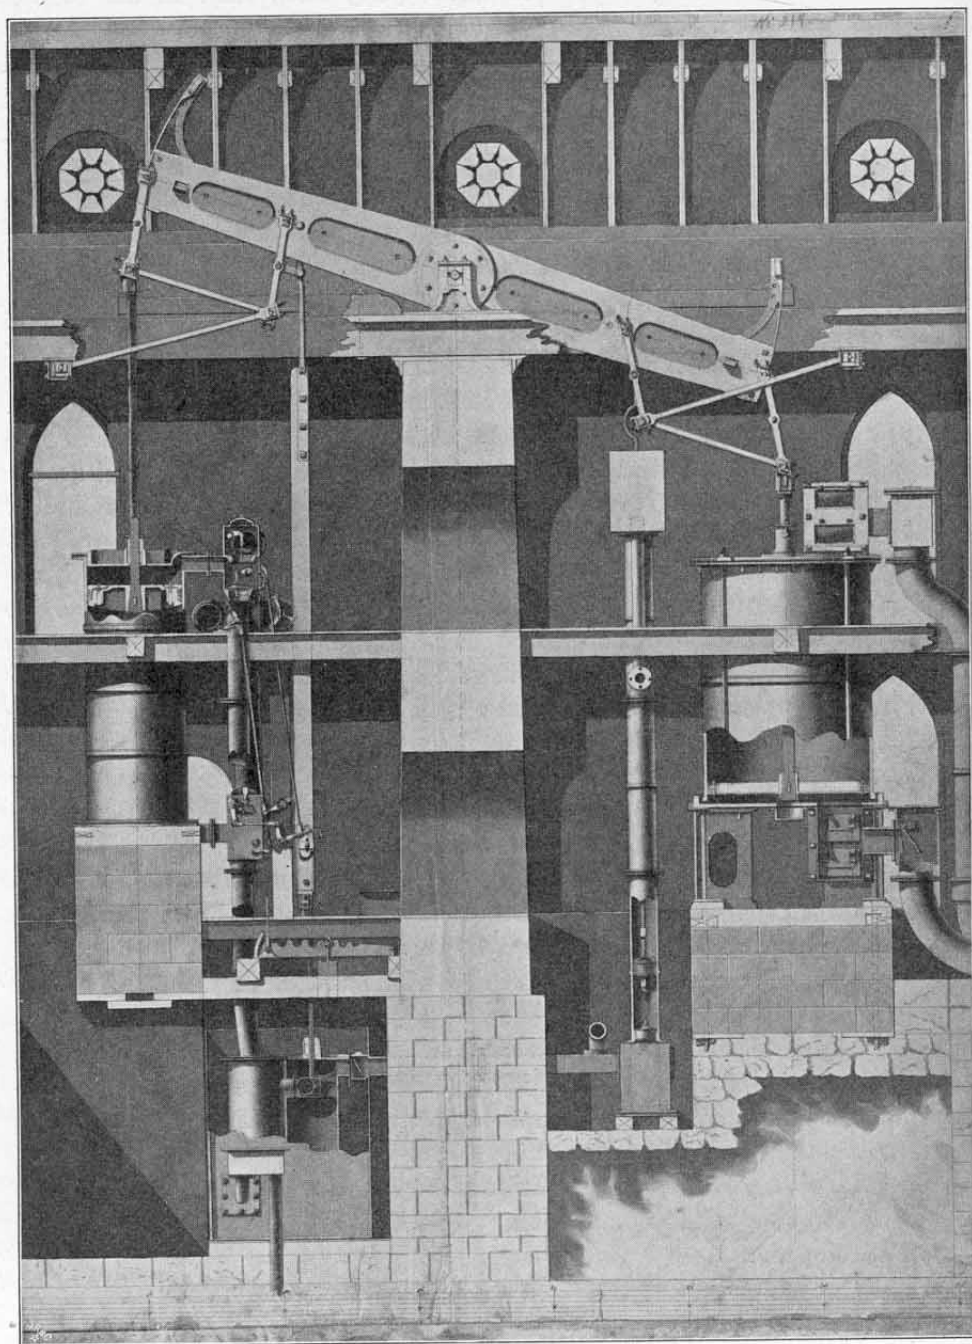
Gebläsemaschine, 1802 von Holtzhausen erbaut.
